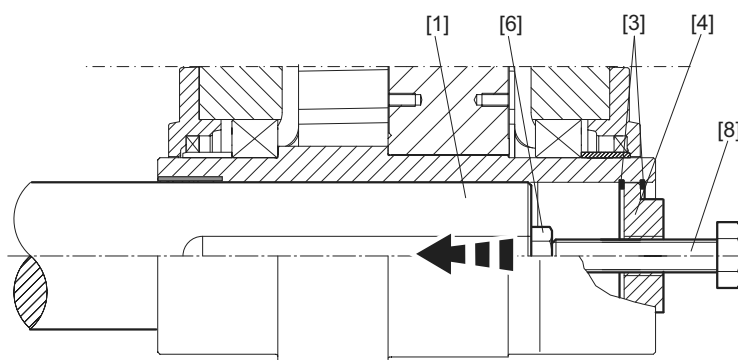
Desmontaje del reductor de eje hueco con unión por chaveta
